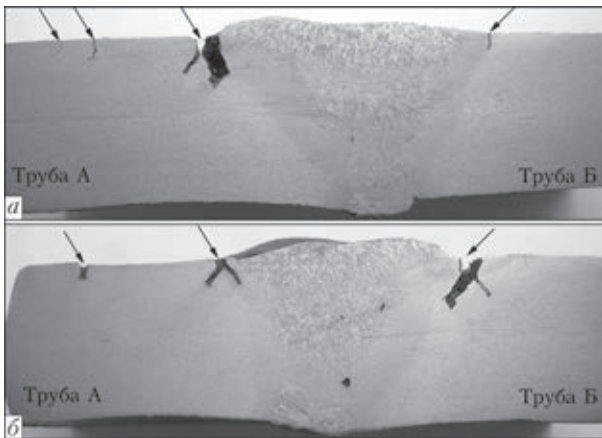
Поперечные макрошлифы кольцевого сварного соединения в зоне повреждения (стрелками показано расположение трещин)
